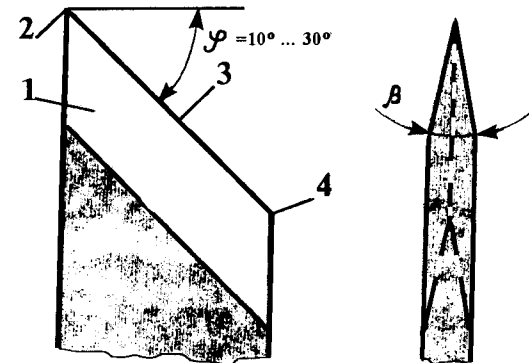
Лезвие плоской косой токарной стамески: 1 — передняя поверхность; 2 — носок; 3 — режущая кромка; 4 — пятка
